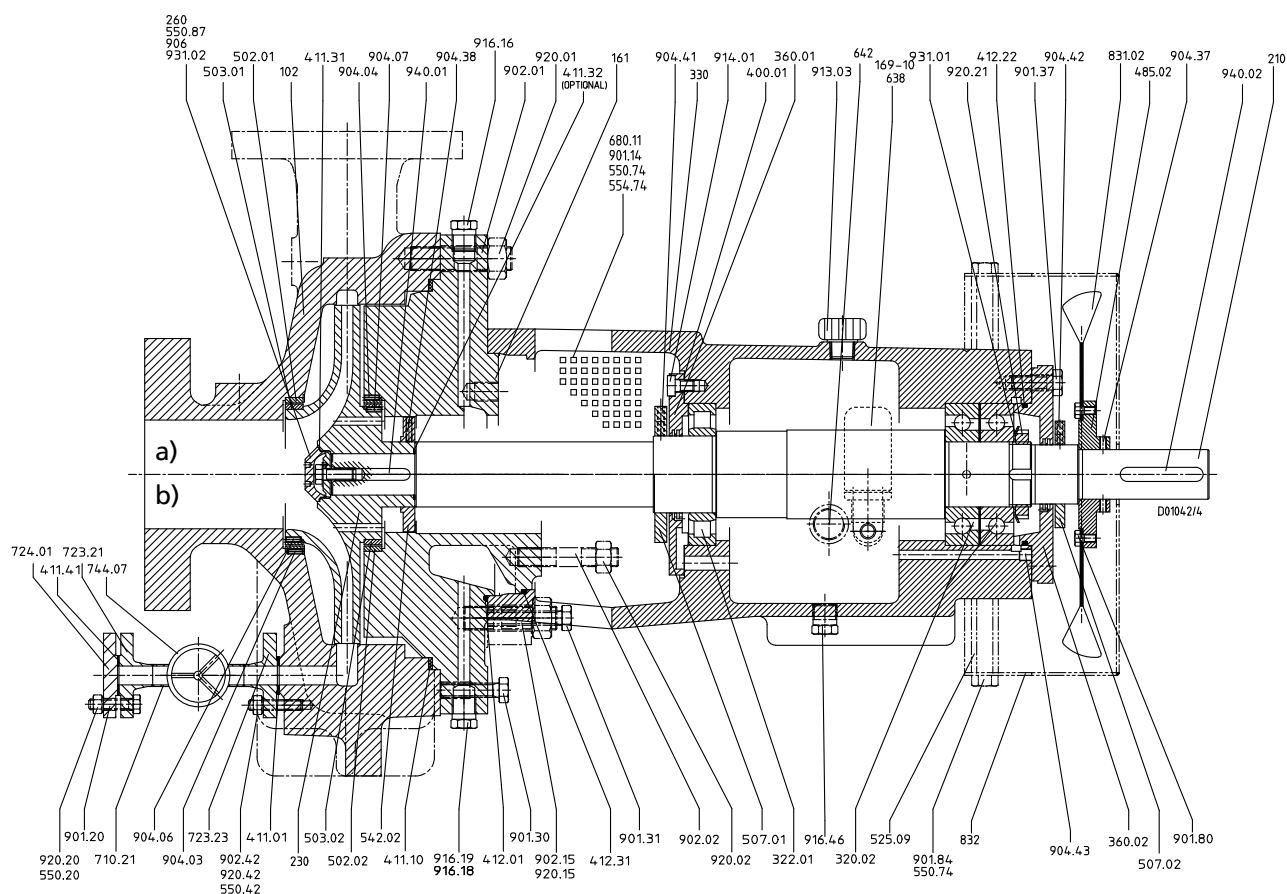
Корпус подшипников B06 и B07, а) без охлаждения и б) с охлаждением
